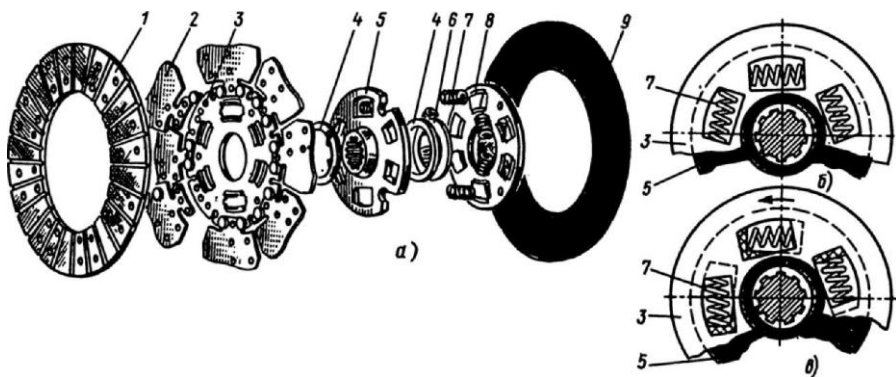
Ведений диск зчеплення: *а* - конструкція; *б, в* - робота демпфера; 1, 9 – накладка з високо фрикційного матеріалу; 2 – металева пластина (сектор); 3 - диск; 4, 6 - кільце; 5 - маточина; 7 - пружина; 8 - диск маточини.
